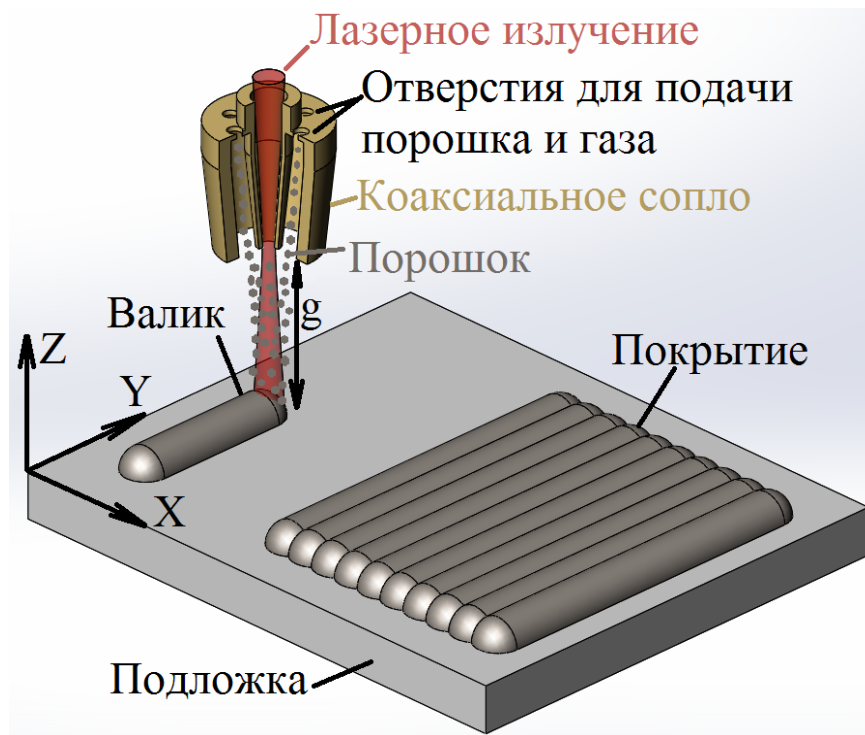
Схематическое изображение коаксиального лазерного нанесения металлического порошка
